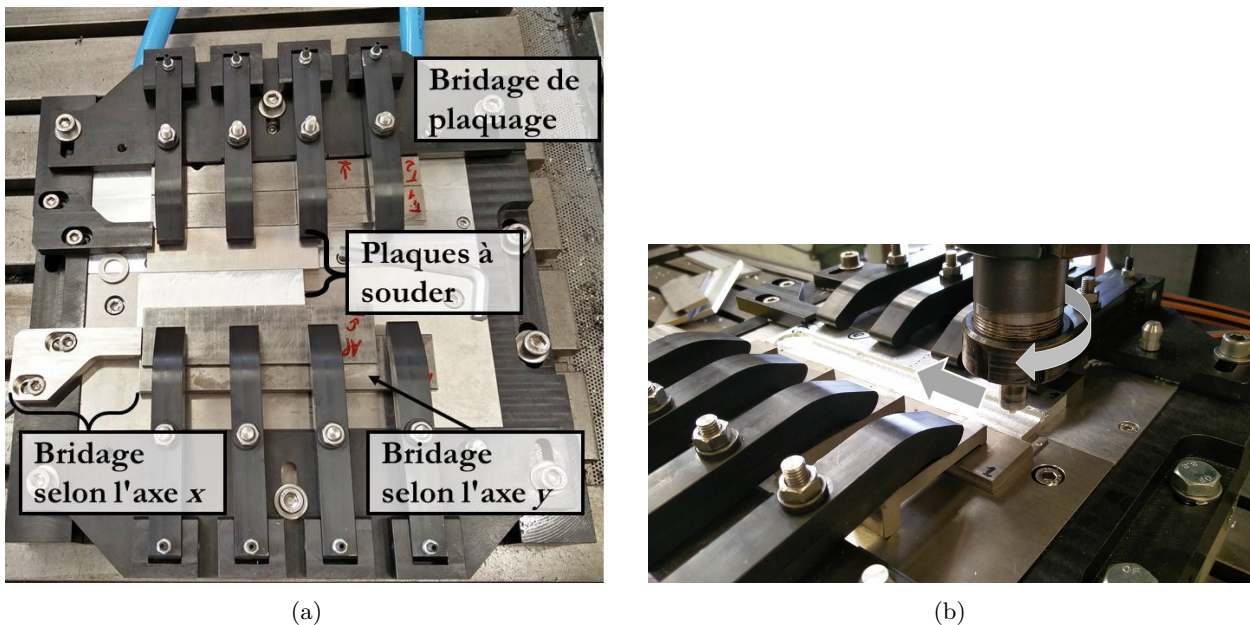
Montage pour la mise en œuvre du procédé FSW. (a) Vue en plongée du montage avec les différents bridages, (b) Vue du bridage avant le début du procédé de soudage.
